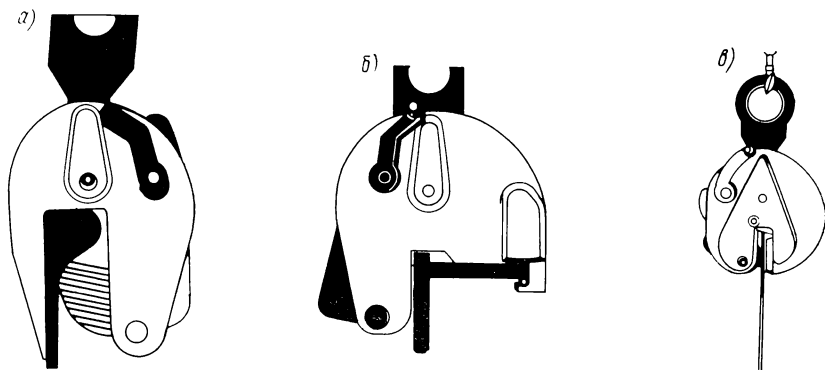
Самозажимные грузозахватные приспособления: а — для полособульбового профиля; б — для углового профиля; в — для полос.
